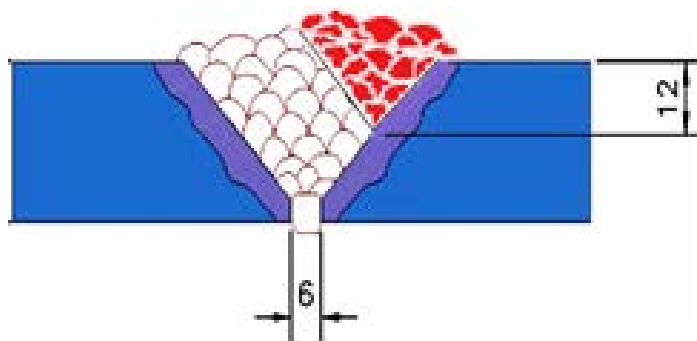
Execução da soldagem aplicando a técnica da meia camada.
